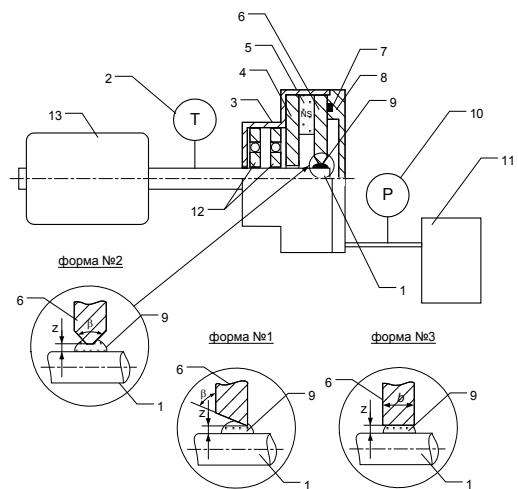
Блок-схема стенда МЖУ: 1 – уплотняемый вал; 2 – тахометр; 3 – корпус МЖУ; 4 – полюс; 5 – постоянный магнит; 6 – исследуемый полюс; 7 – резиновое уплотнение; 8 – крышка; 9 – магнитная жидкость; 10 – вакуумметр; 11 – вакуумный насос; 12 – подшипники; 13 – электродвигатель
